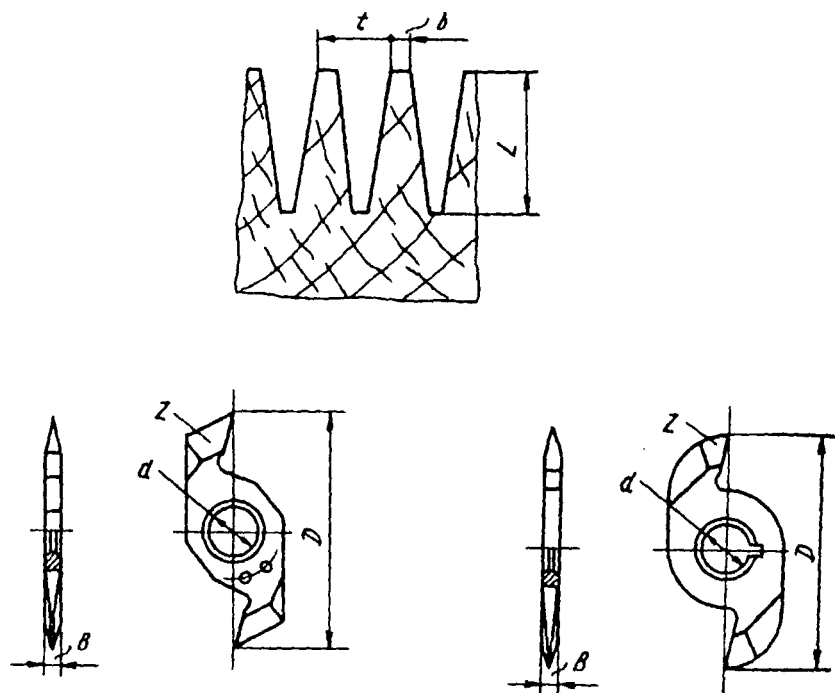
Фрезы для обработки зубчатых шипов:
